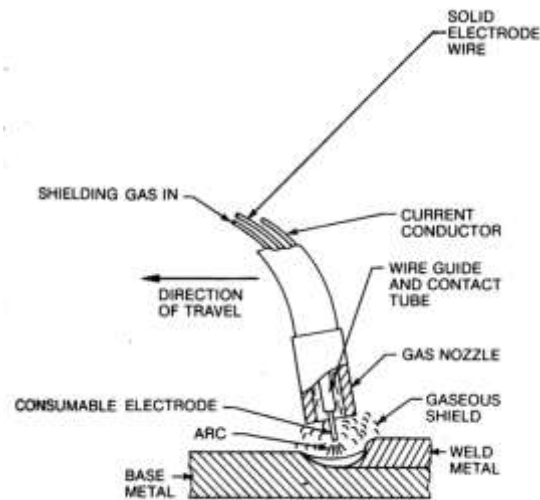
GMAW: GAS METAL ARC WELDING
